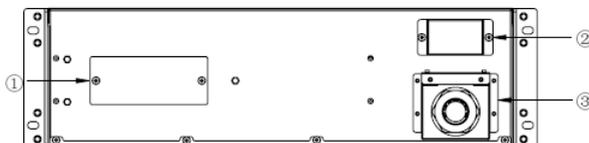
Vue de la face arrière du module batterie OLS6000/10000ERT6U(M)
